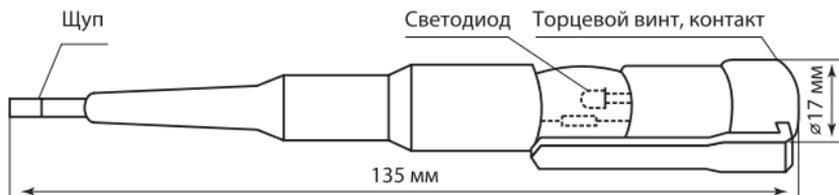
Габаритные размеры и основные элементы отвертки-пробника ОП-1
